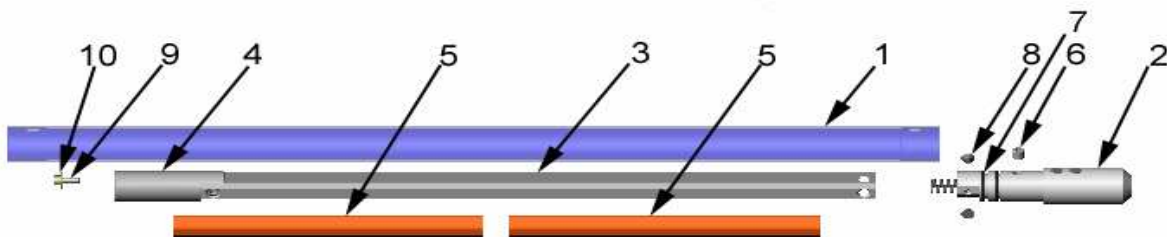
Outil de coupe Split Shot Cutter avec rails - Vue éclatée
